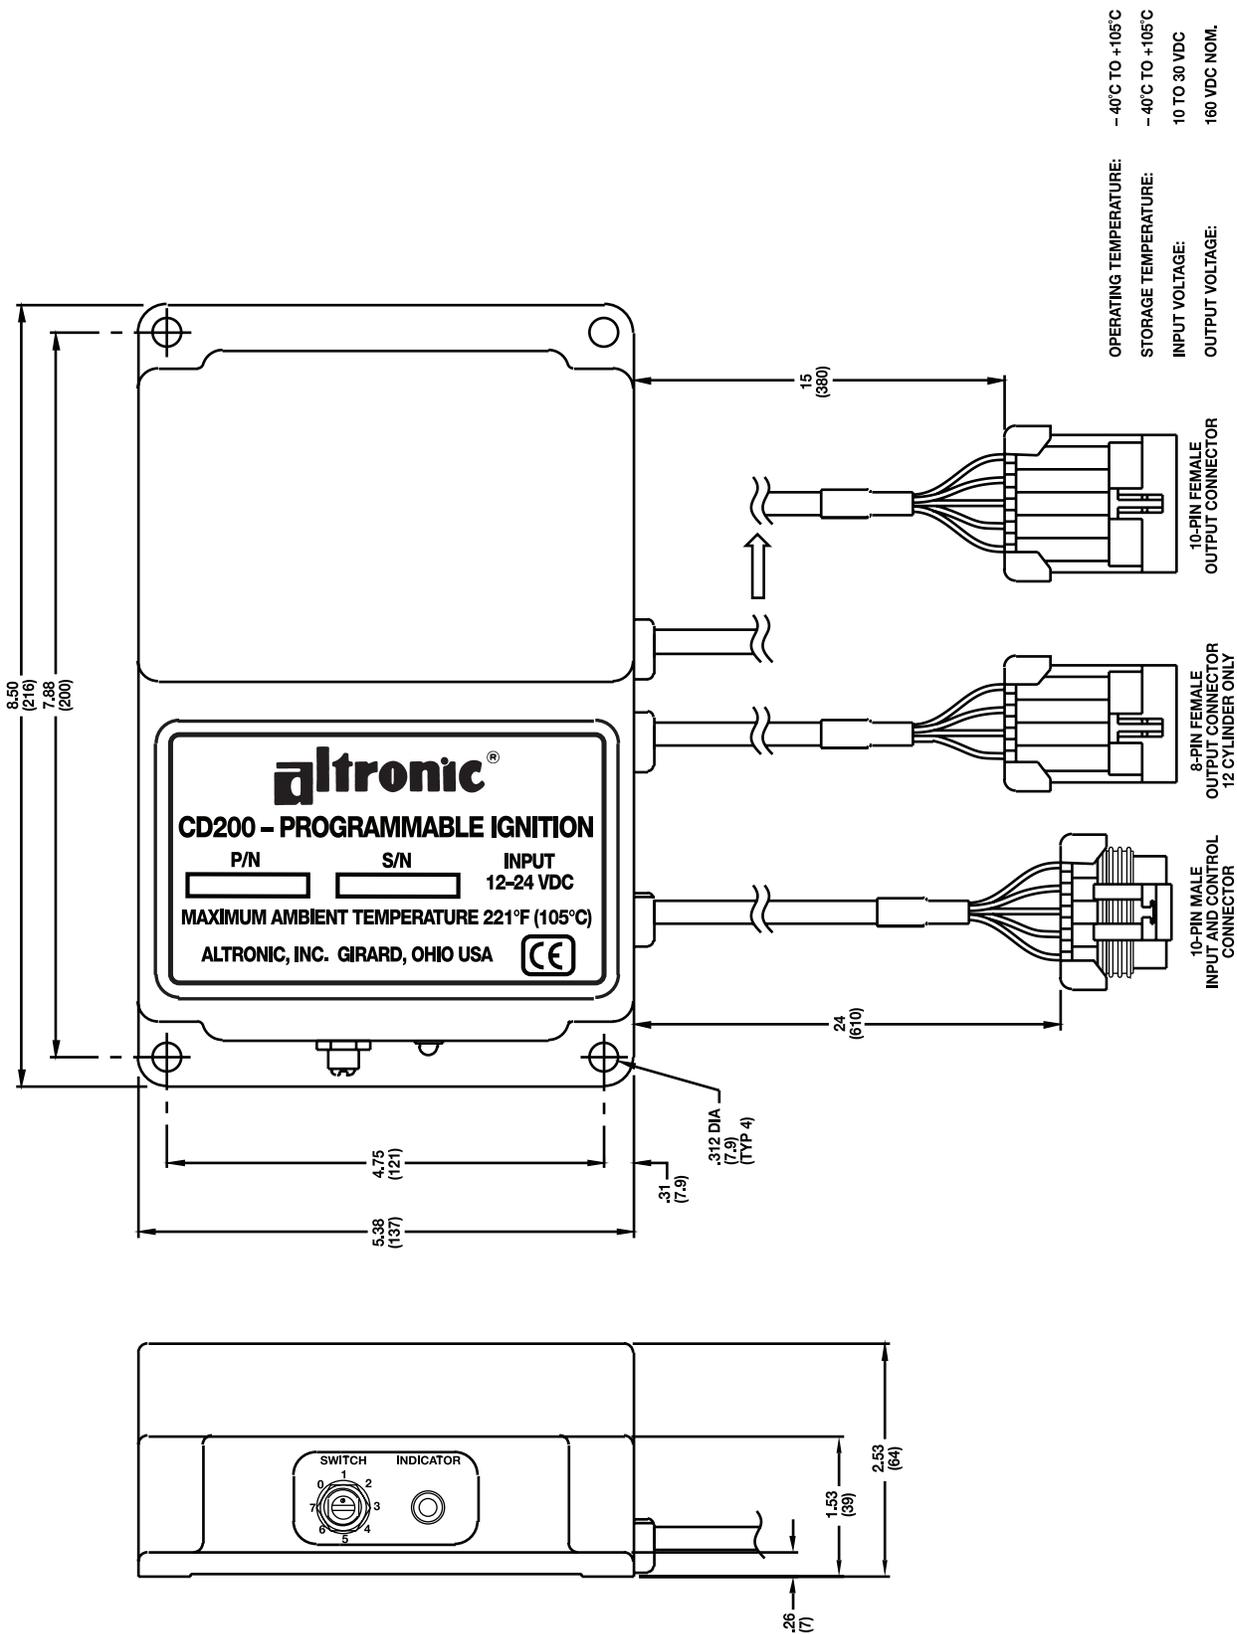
SPECIFICHE E DIMENSIONI, 791080-X
